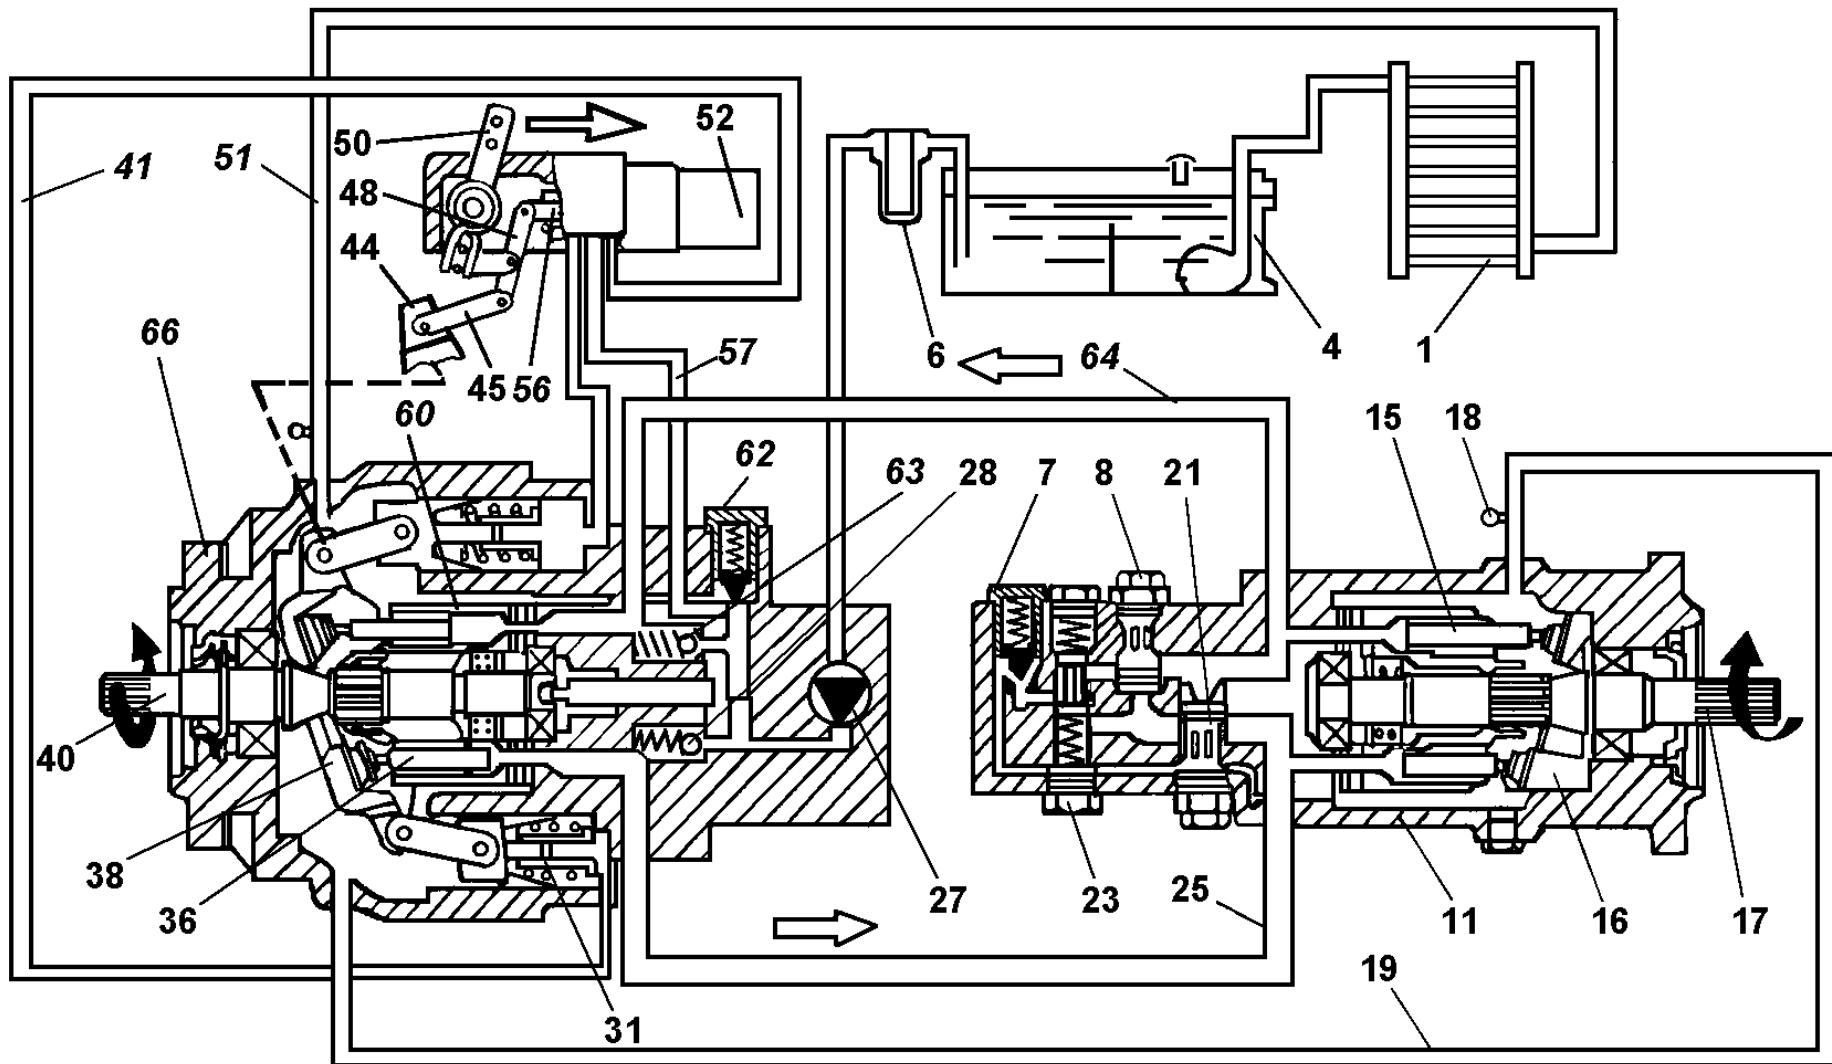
Конструктивная схема передачи ГСТ-90 (движение назад) (обозначения см. рис. 2.34)
